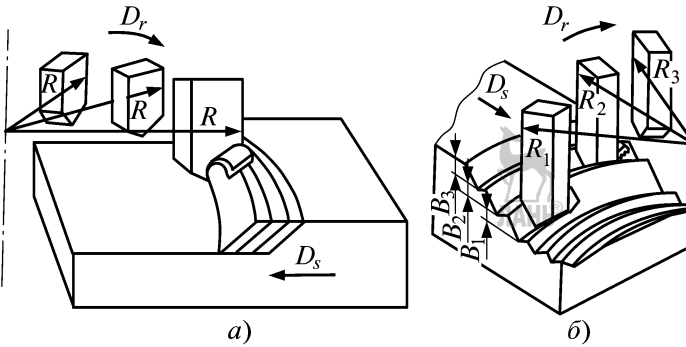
Схемы расположения зубьев у торцовых фрез
